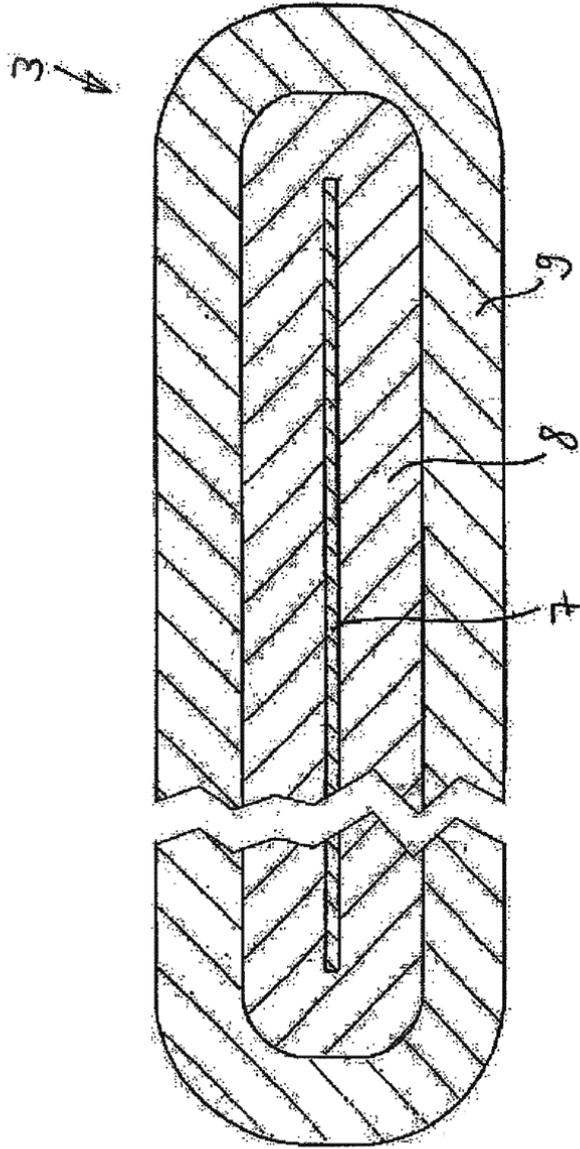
Sección longitudinal de la banderilla (15) B-B'
